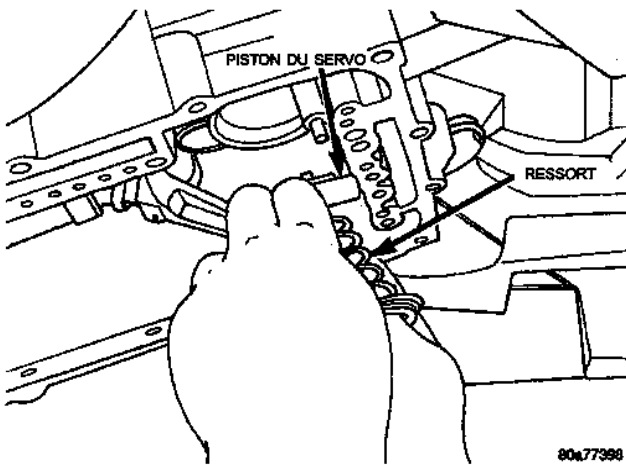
Ensemble de servo de gamme basse/marche arrière
